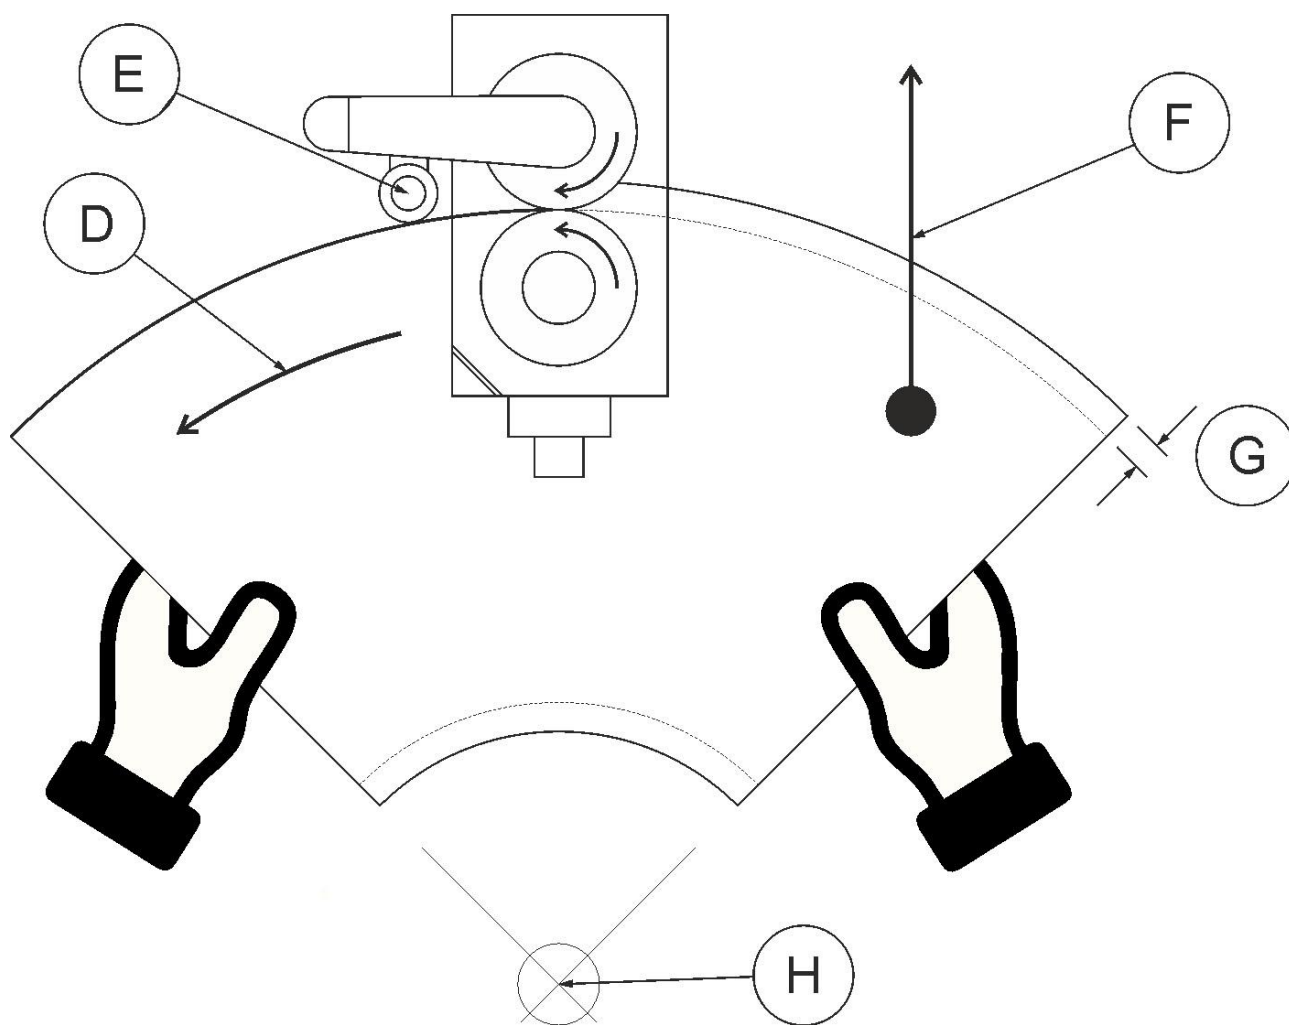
Устройство отбортовки радиусных кромок (вид сверху).
